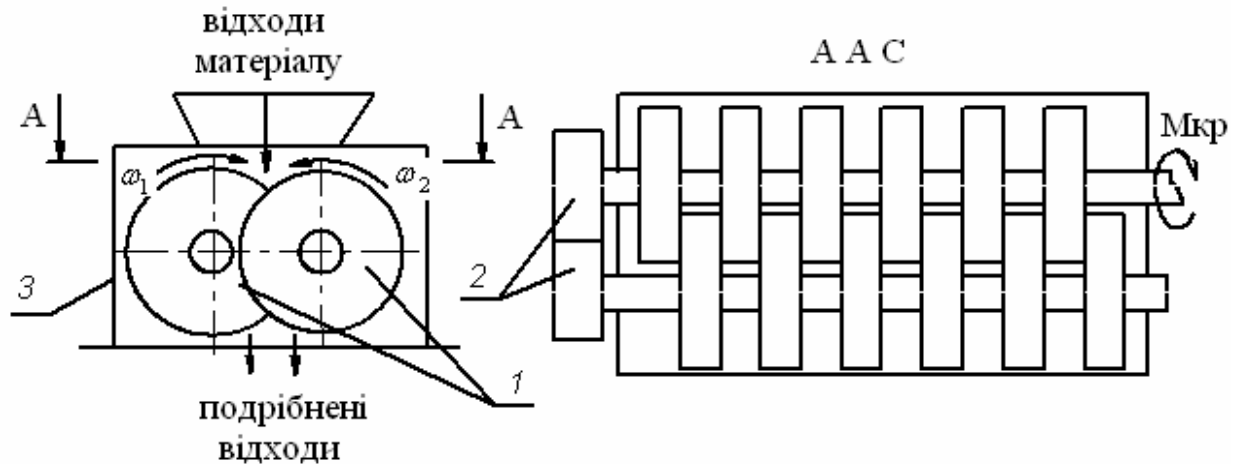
Дисковий подрібнювач: 1 – диски;
